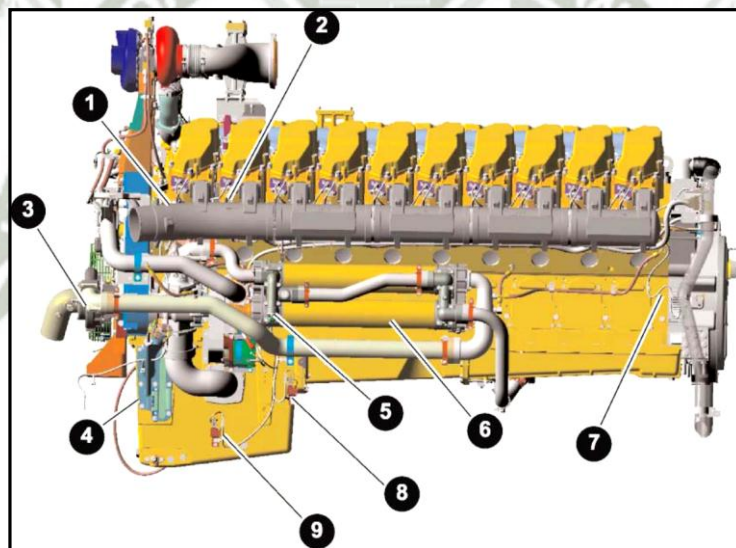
Motor Diésel Costado Izquierdo del Motor
